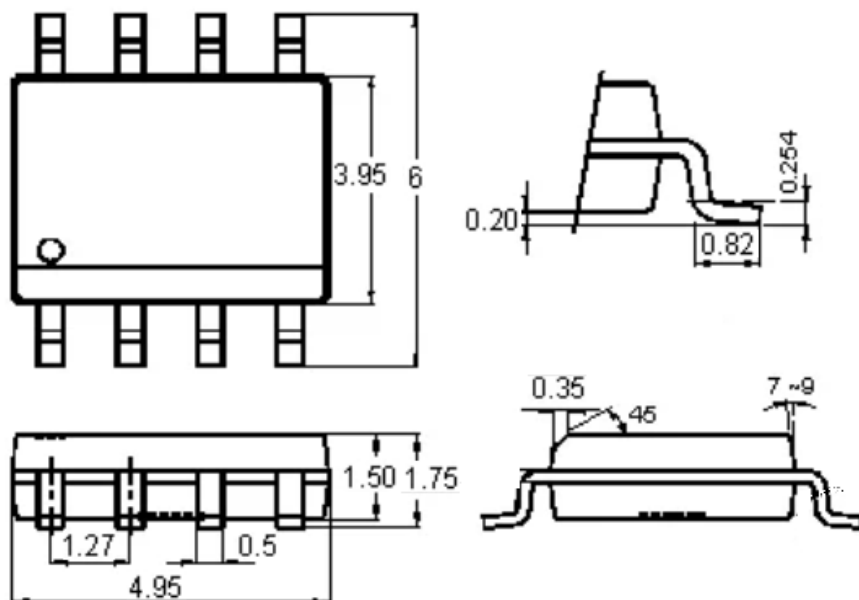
Габаритні розміри корпуса SOP-8
